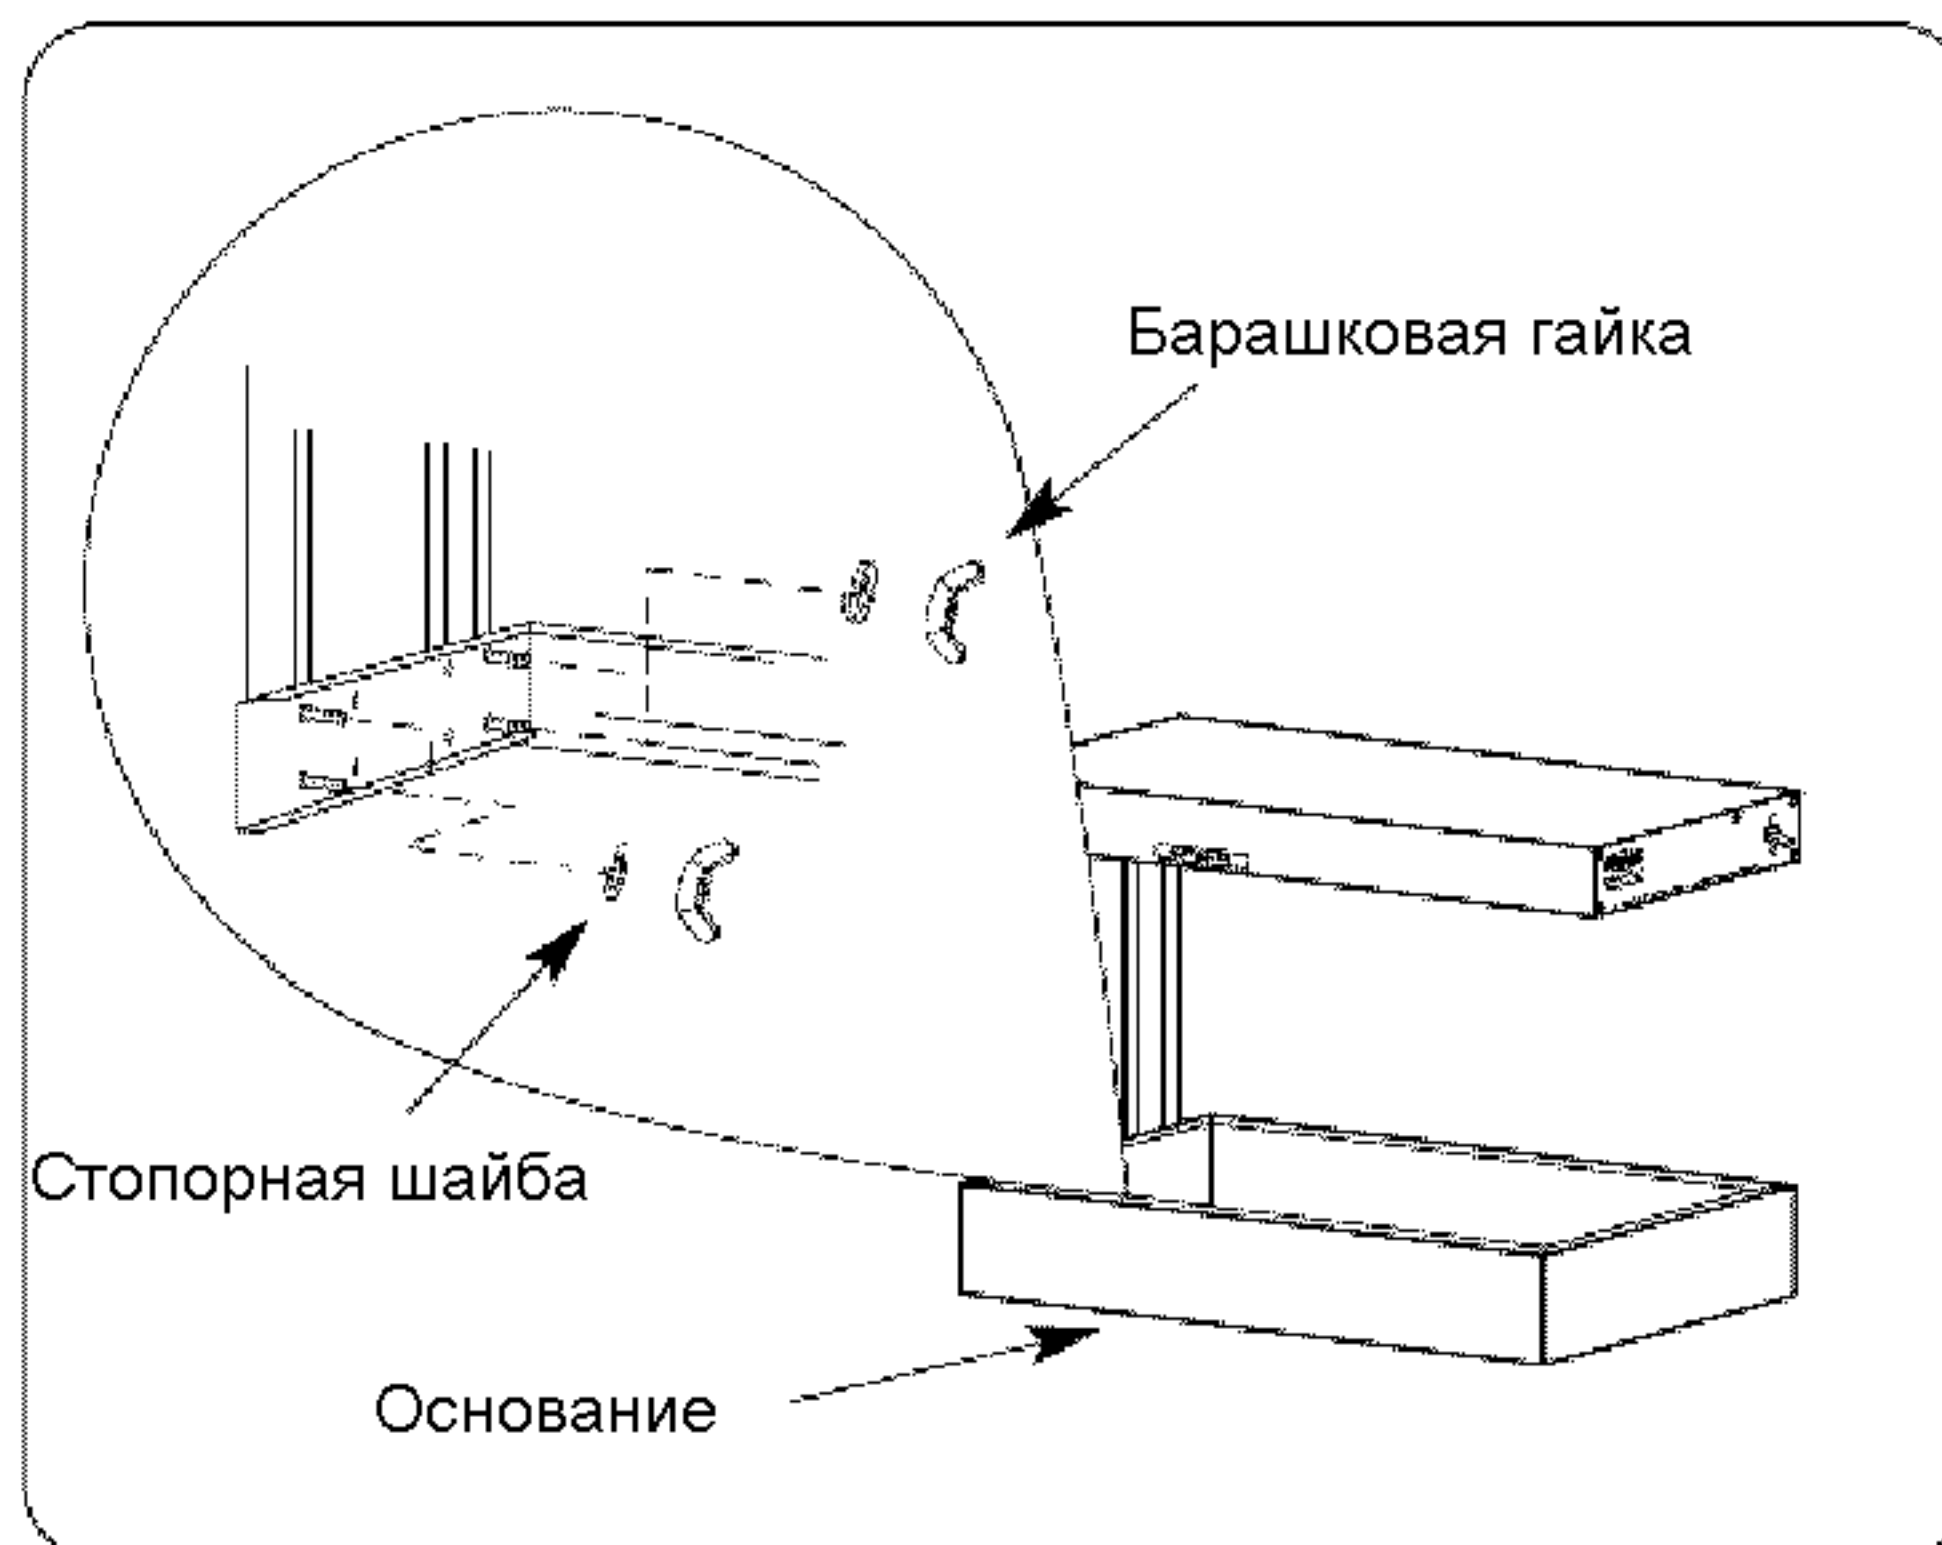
Сборка верхнего корпуса с опорными консолями и основания
